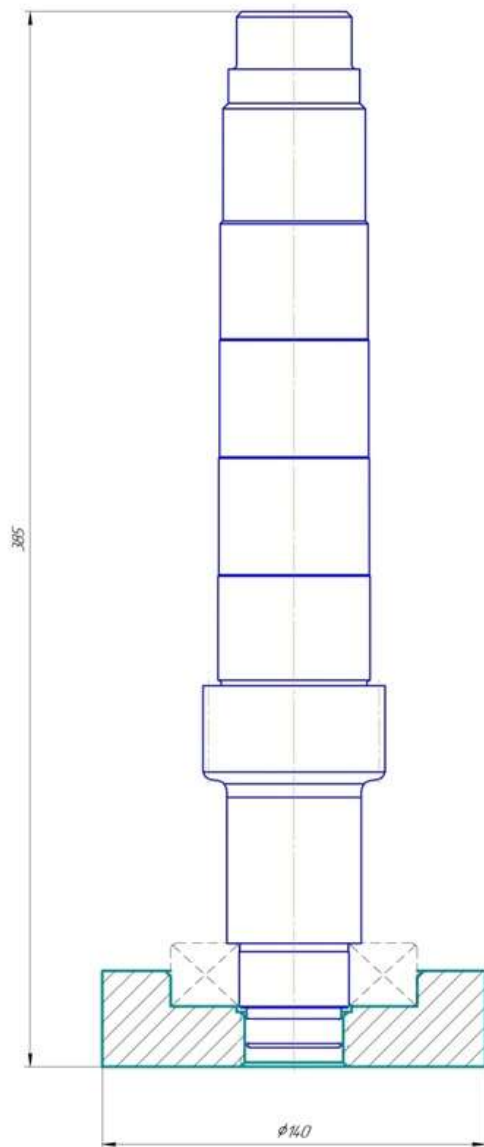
Центрирующее приспособление для сборки деталей клеевого соединения «промежуточный вал-подшипник» коробки передач КАМАЗ-4310
